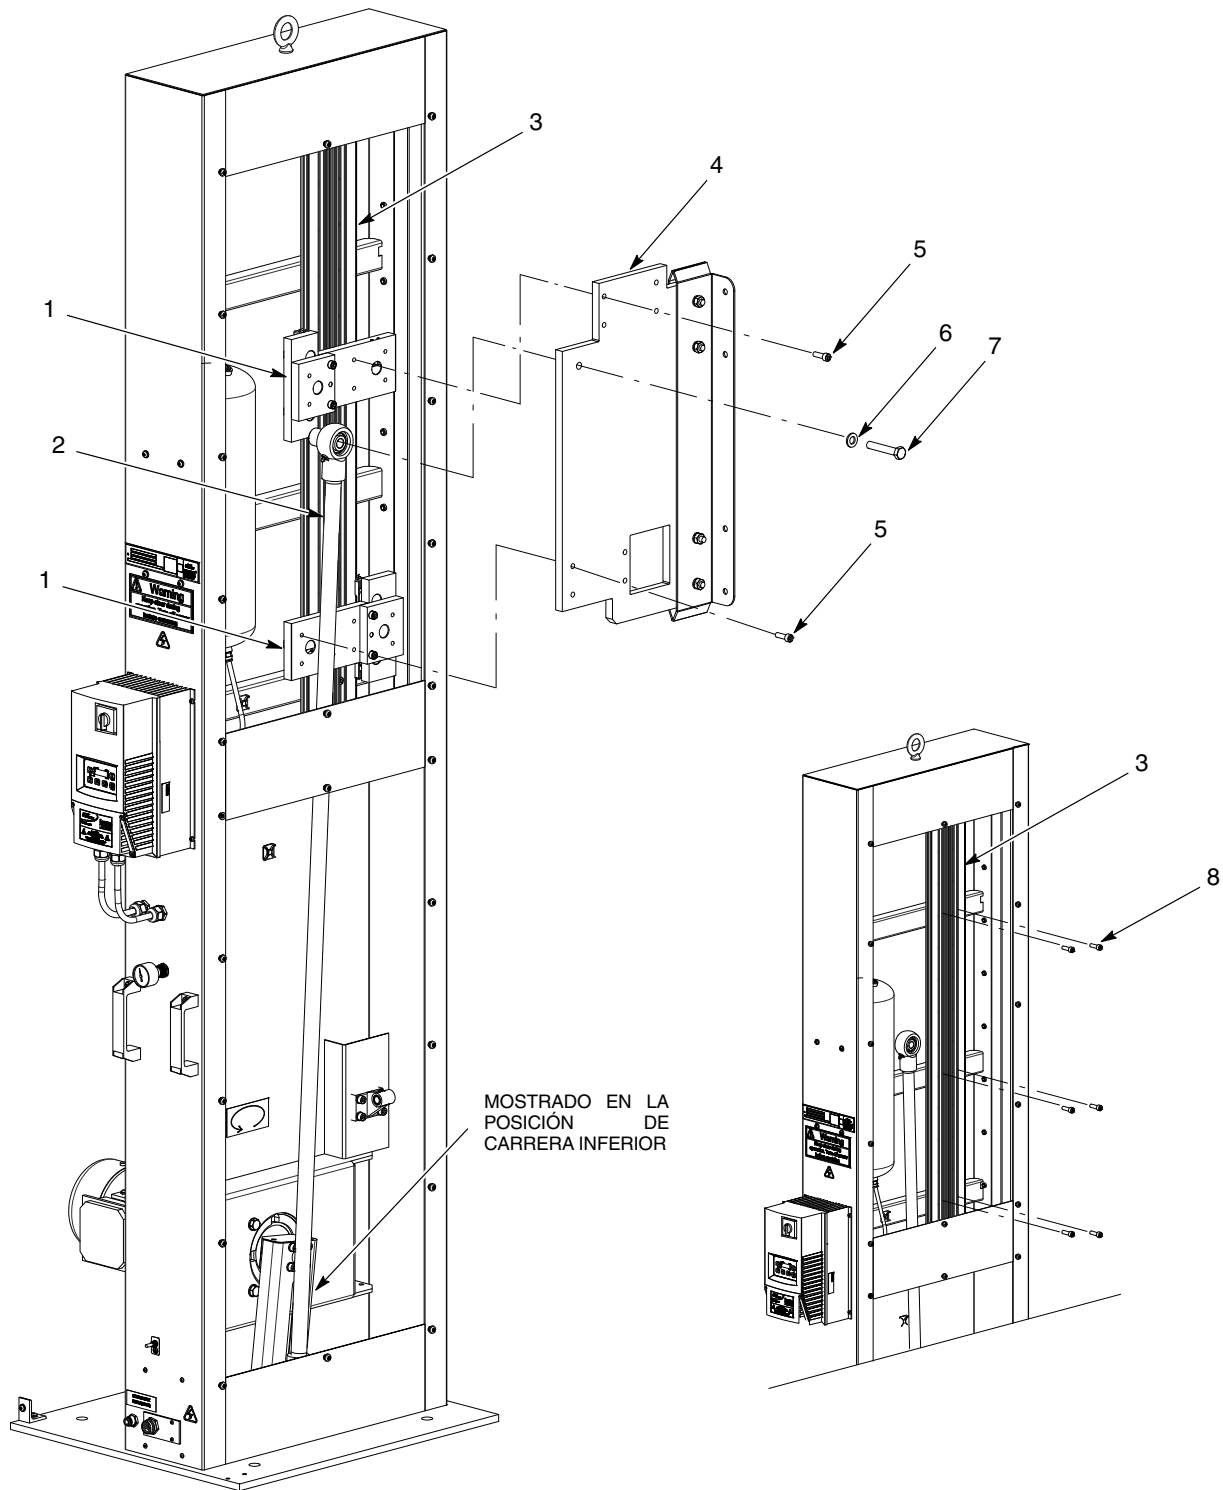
Instalación del carro y montajes de la placa de montaje de la pistola
